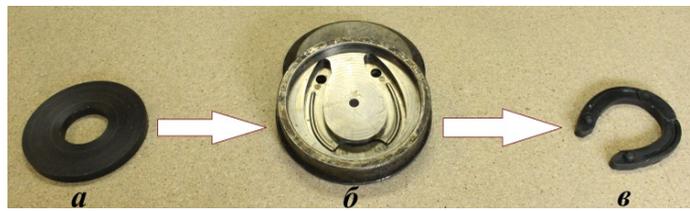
Схема изготовления подковы из заготовки СВМПЭ твердофазной объемной штамповкой:
